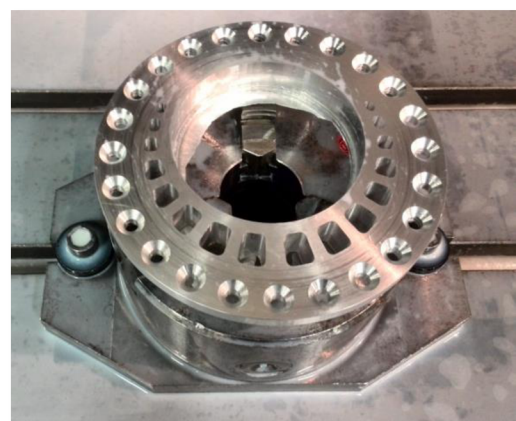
Tvar součásti po obrobení frézou o Ø 3 mm.
